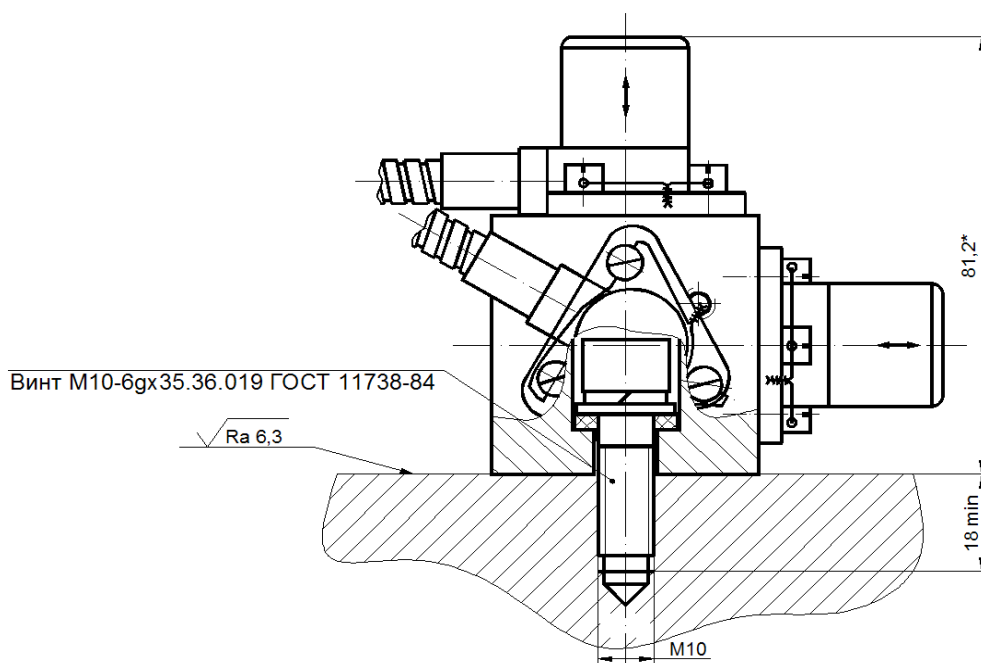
Установка датчика пьезоэлектрического ДПЭ23МВП на опоре подшипника
